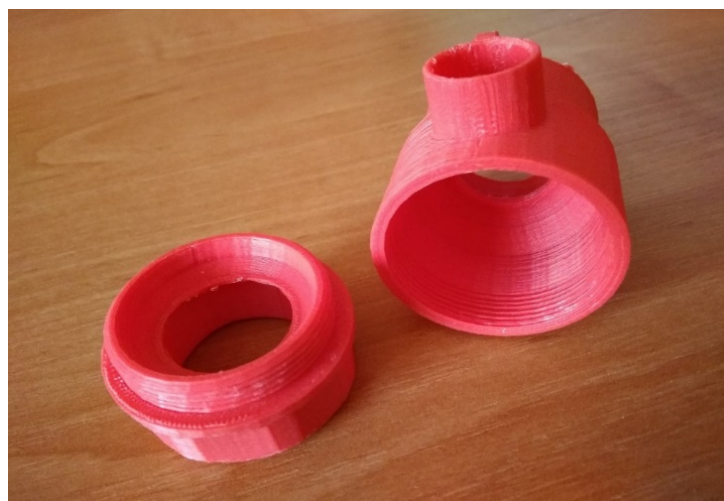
Прототипы деталей крышки и корпуса шарового крана ДУ 25
